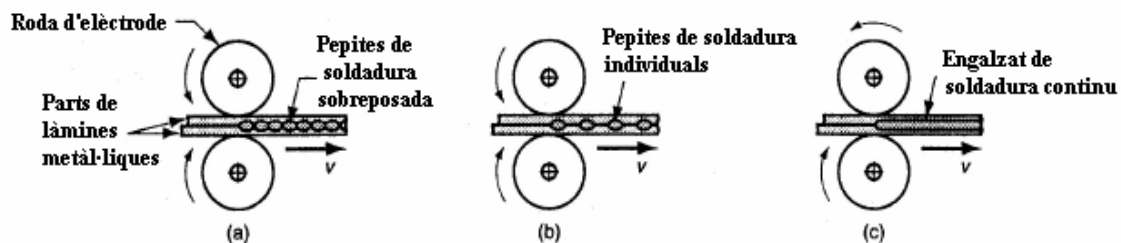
Soldadura d'engalzat per resistència (RSEW).
